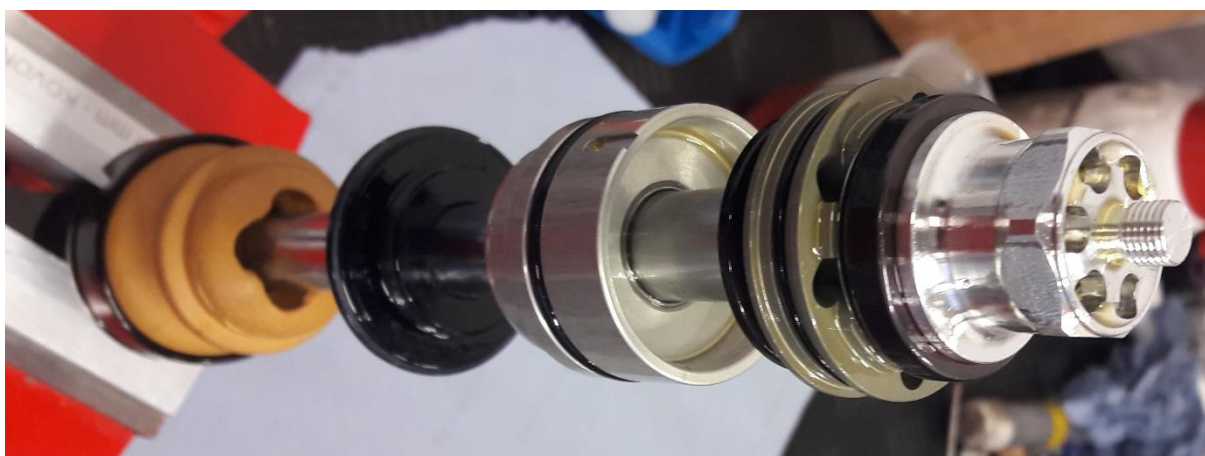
1 - Planžetový ventil tlumiče FRT40
